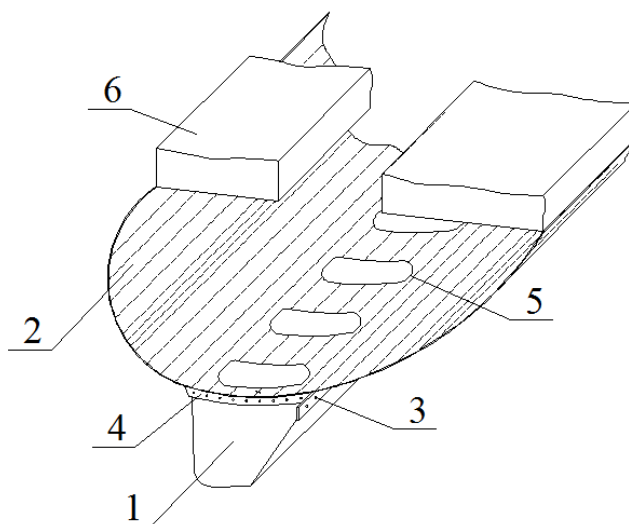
Конструкция ГО воздушной подушки: 1– навесной элемент; 2 – гибкий ресивер; 3 – поперечный комингс; 4 – продольный комингс; 5 – воздухоотводные отверстия; 6 – жесткий корпус
